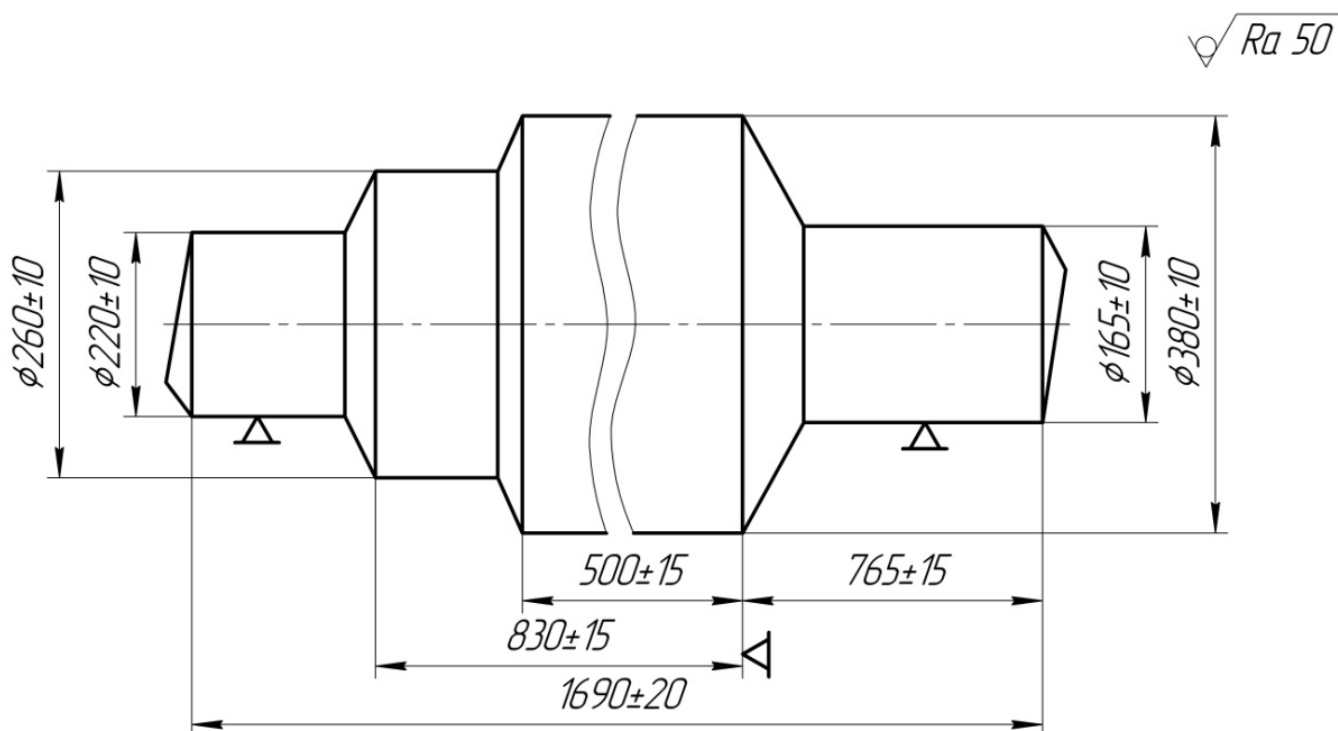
Заготовка, що виготовлена ковкою на молоті
